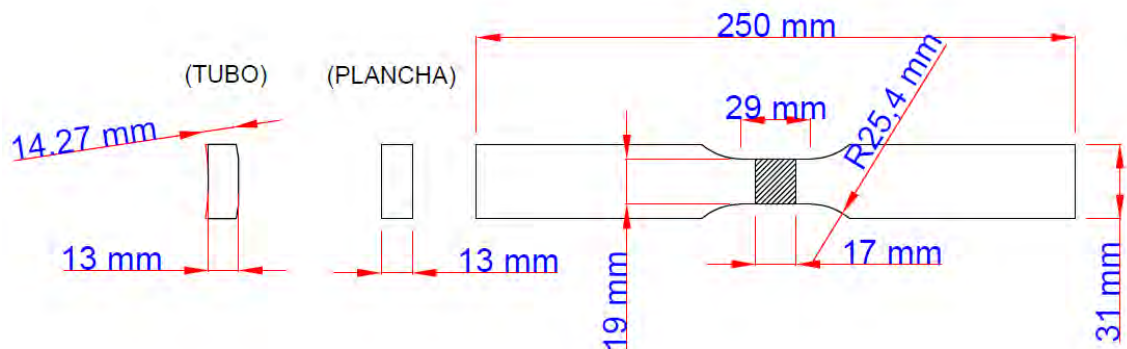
Dimensiones de la probeta para el ensayo de tracción
